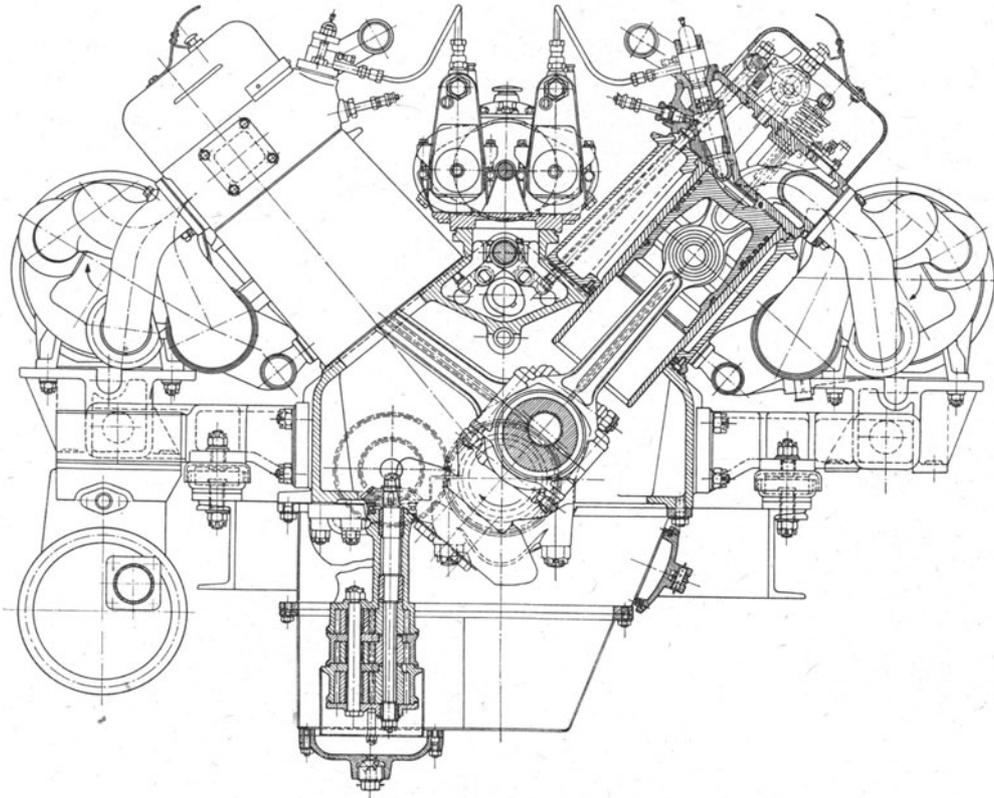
Triebwagenmotor R 12 a der Simmeringer Maschinen- und Waggonbau AG.
